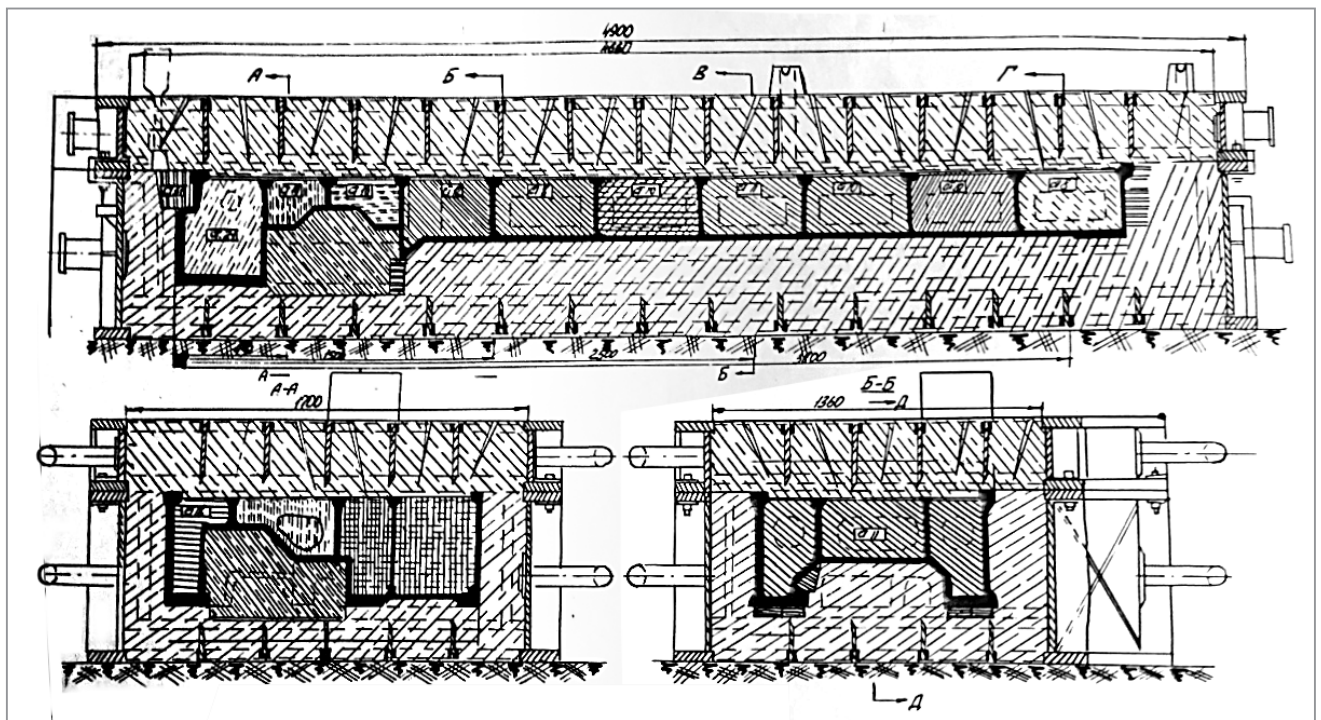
Схема сборки формы станины расточного станка с верхней опокой
